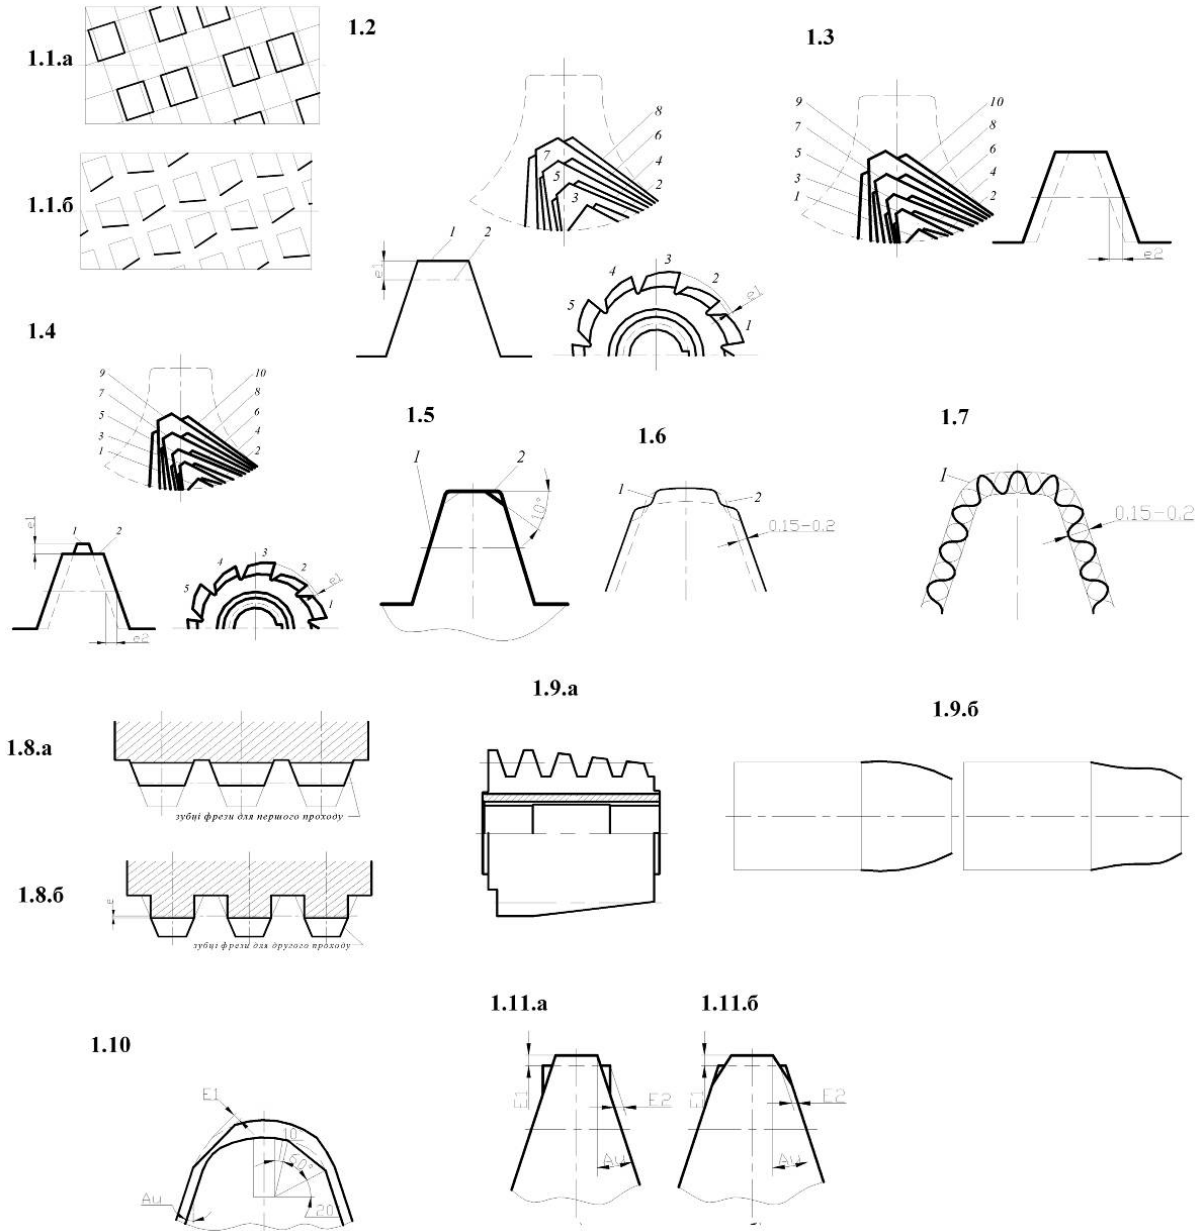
Схеми черв'ячних фрез з прогресивною
